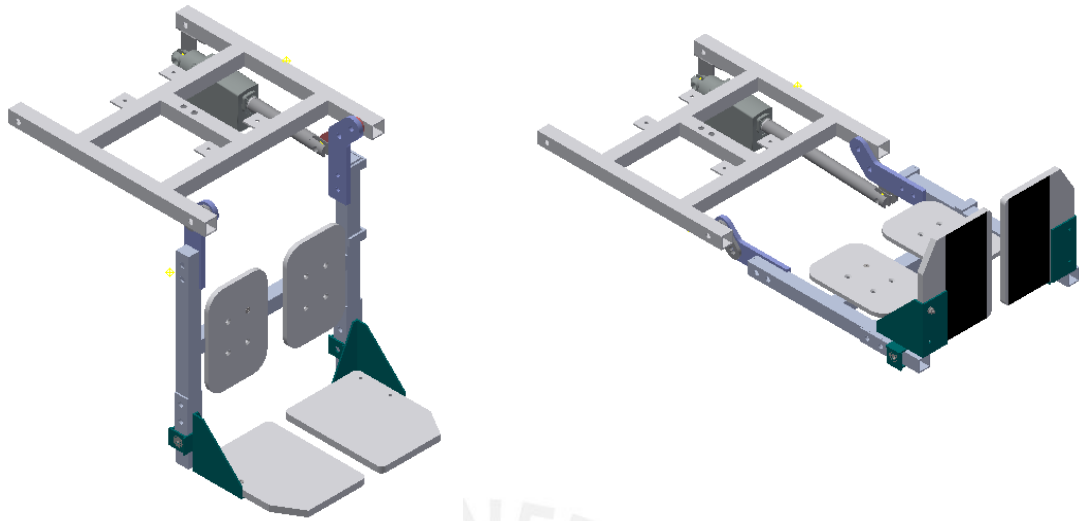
Giro del apoyapié - Vista isométrica de la posición inicial y final
